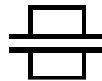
Símbolo para soldadura de conexión y óvalos
